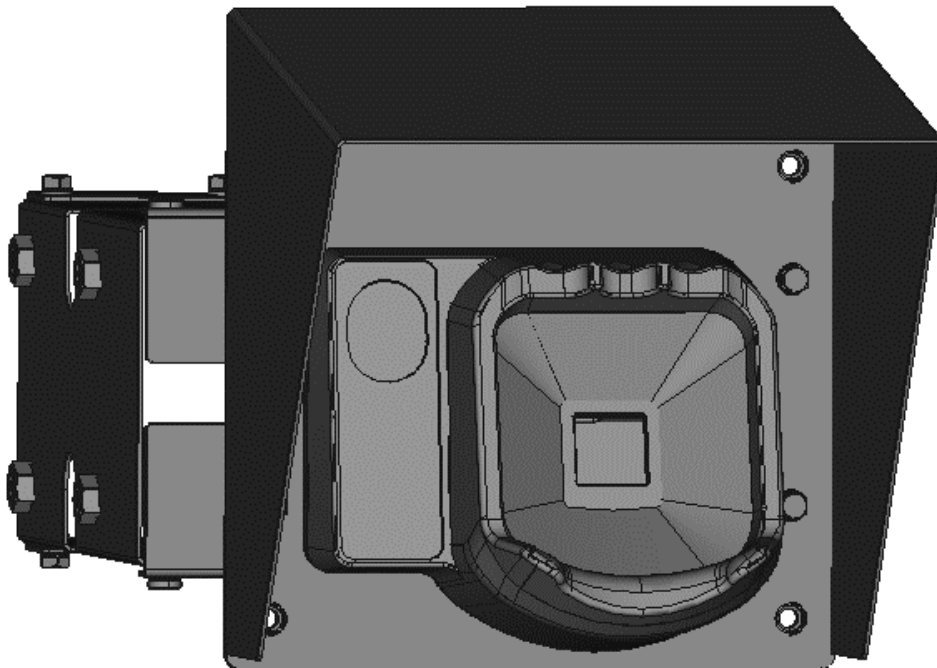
Внешний вид козырька в сборе со считывателем
